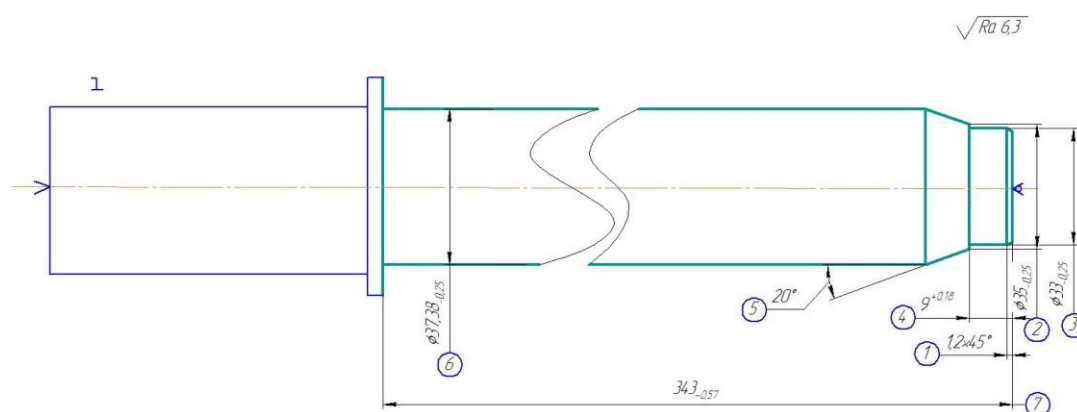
Закріплення заготовки в патроні та в обертовому центрі при виконанні токарних операцій
